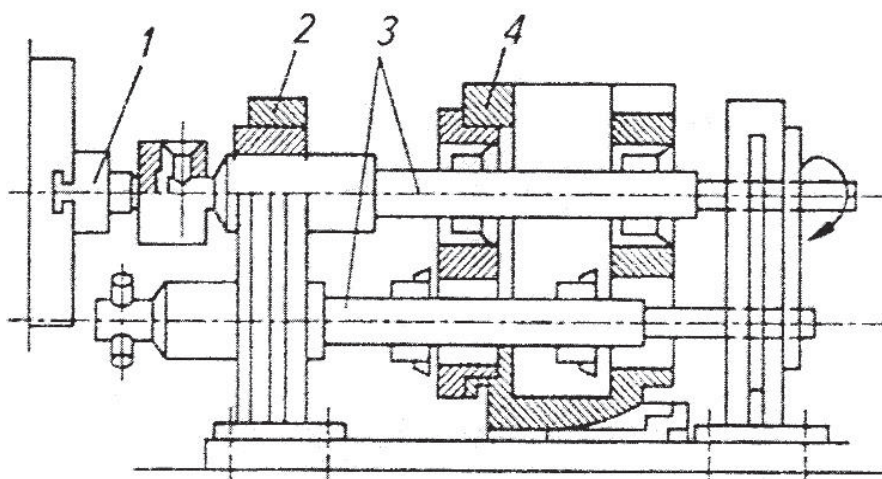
Схема расточки отверстий в корпусной детали по кондуктору:
